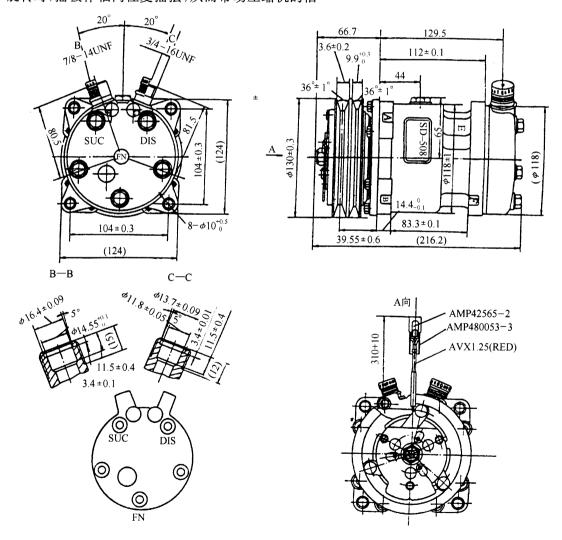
SE5H14 型压缩机外形尺寸 后盖为 FN 型,具体结构是接口向上,O 形环接口,尺寸 3/4in×7/8in. 无充气口
